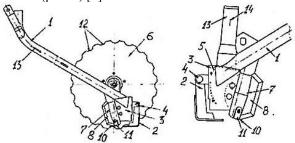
Однодисковый сошник с вырезным диском: I — семяпровод; 2 — клапан; 3 — корпус; 4 — шарнирное соединение; 5 — отражатель; 6 — диск; 7 — нож; 8 — передняя кромка ножа трапецеидальной формы; 9 — продольная угловая выемка ножа; 10 — рабочая кромка ножа; 11 — защитная пластина на рабочей кромке ножа; 12 — выемки радиальной формы; 13 — труба-воздуховод
